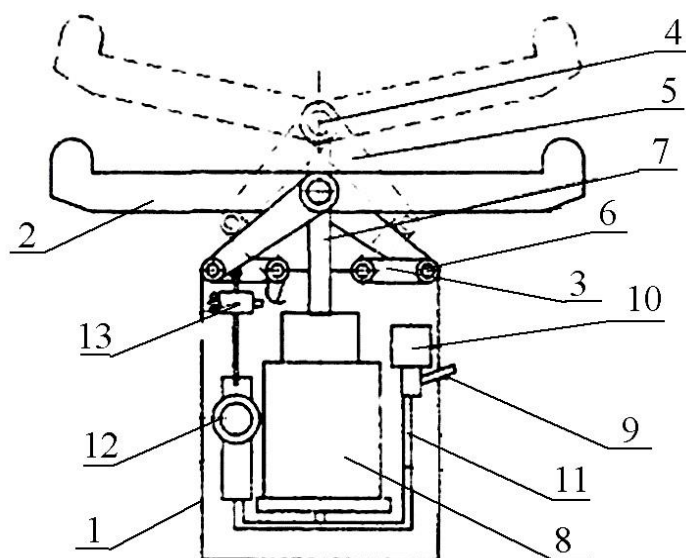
Пневматический бревносбрасыватель СБГ-2:
